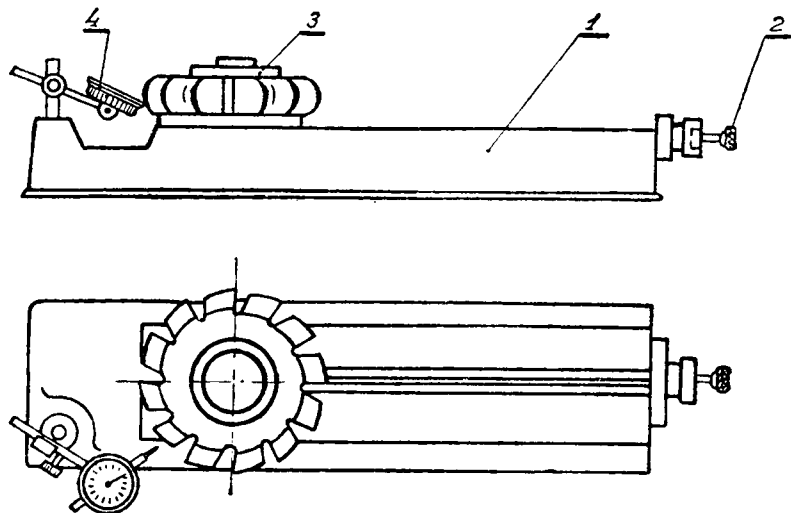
Приспособление для измерения биения зубьев фрез с задней заточкой
